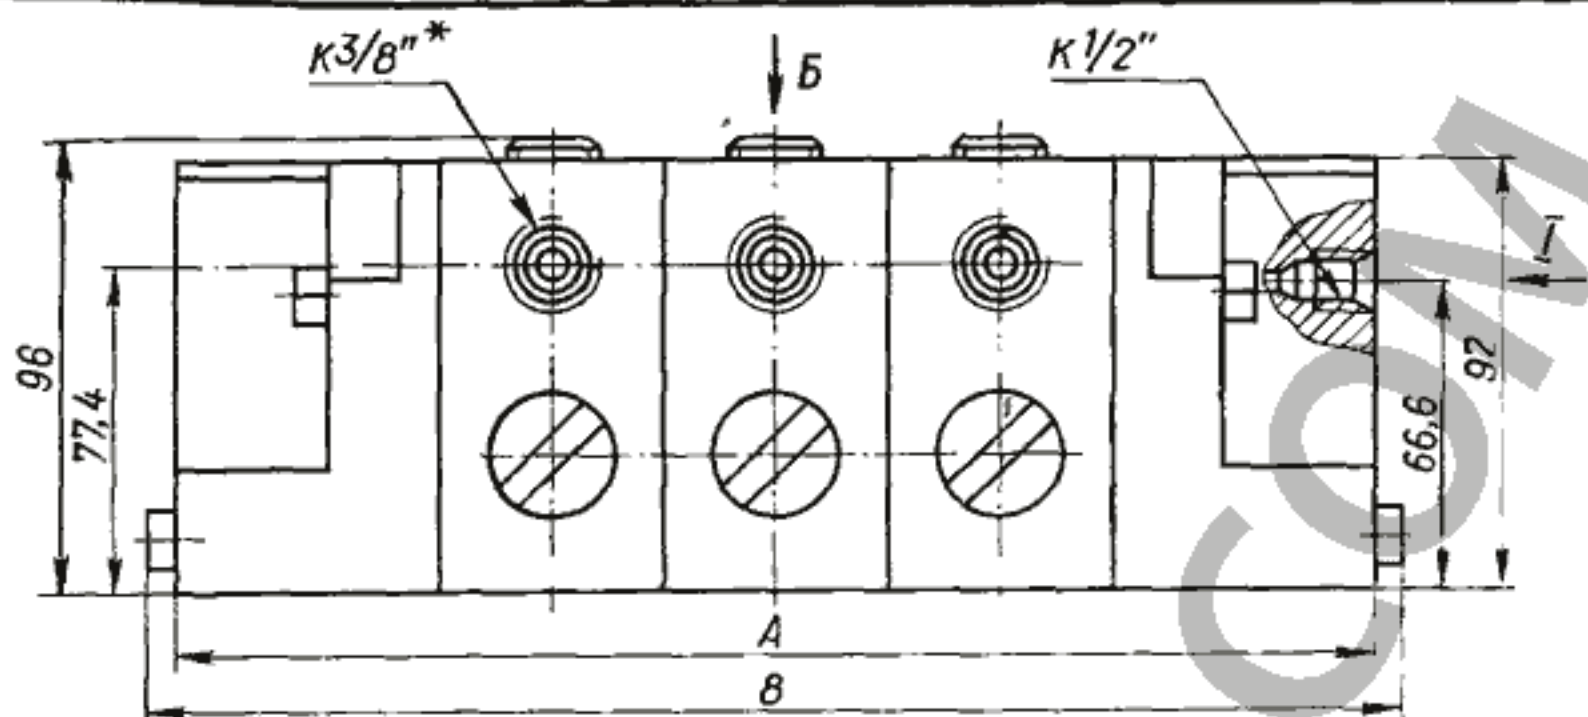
Габаритные и присоединительные размеры питателя типа МГ(О):
